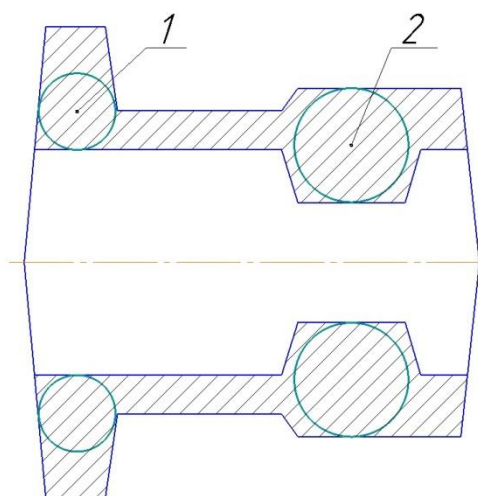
Анализ конструкции отливки «Корпус»
